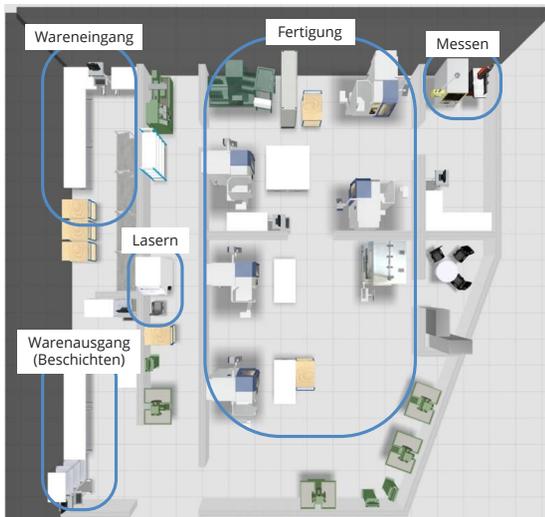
Layout Gerhard Grind GmbH (Darstellung mit visTABLE):
